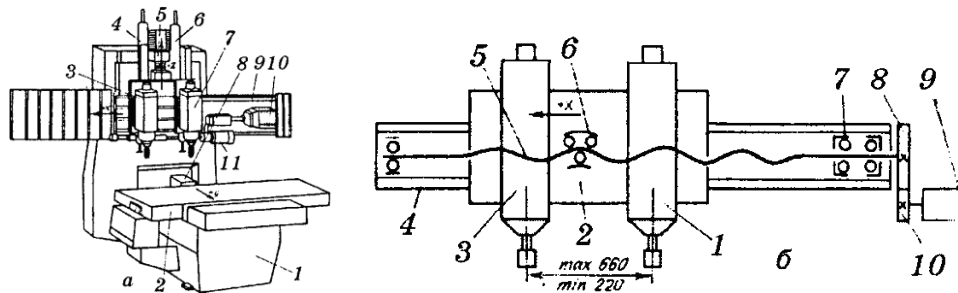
Двошпиндельний вертикально-фрезерний обробний центр з ЧПК: *а* – загальний вигляд: 1 – станина; 2 – стіл; 3, 7 – шпиндельні головки; 4, 6 – пневмоциліндри; 5, 8, 10 – крокові приводи передач; 9 – напрямні; 11 – електродвигунний привод; *б* – фрагмент кінематичної схеми: 1, 3 – шпиндельні головки; 2 – каретка; 4 – напрямні; 5 – гвинт; 6 – кулькогвинтова передача; 7 – підшипники; 8, 10 – косозуба передача; 9 – електродвигун
